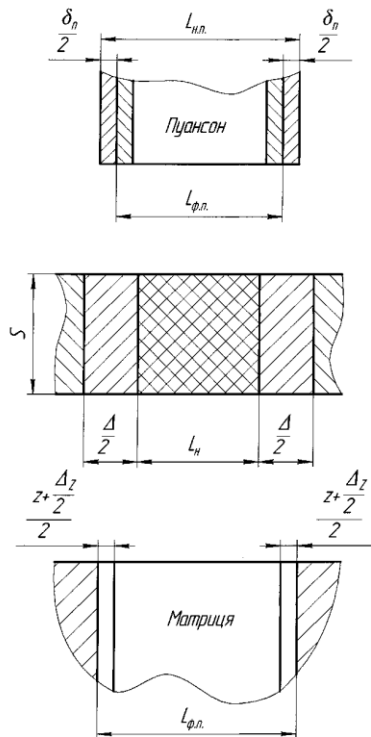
Схема розмірів та полів допусків деталі, що штампується та деталей штапу
